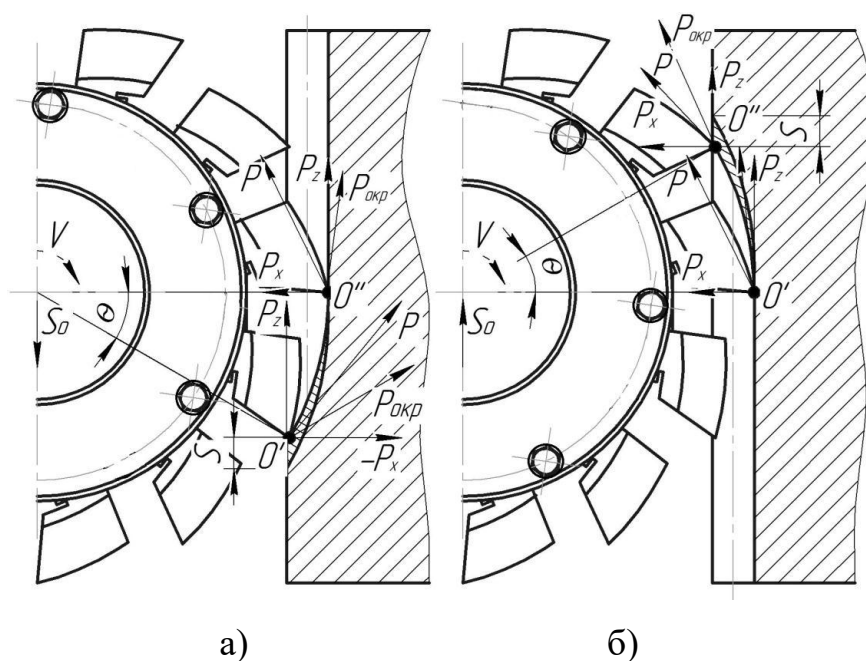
Виды зубофрезерования: а) – встречное; б) – попутное
